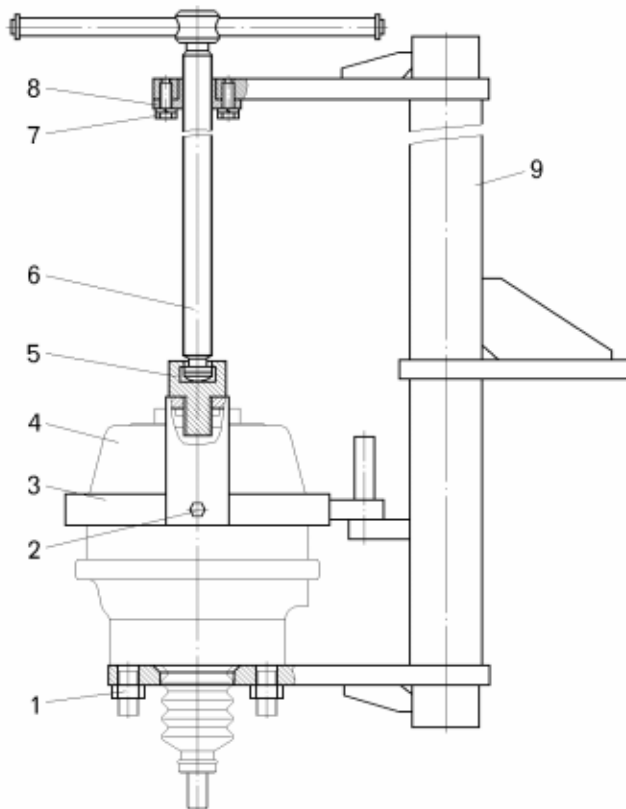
Приспособление для разборки и сборки цилиндра стояночного тормоза:
